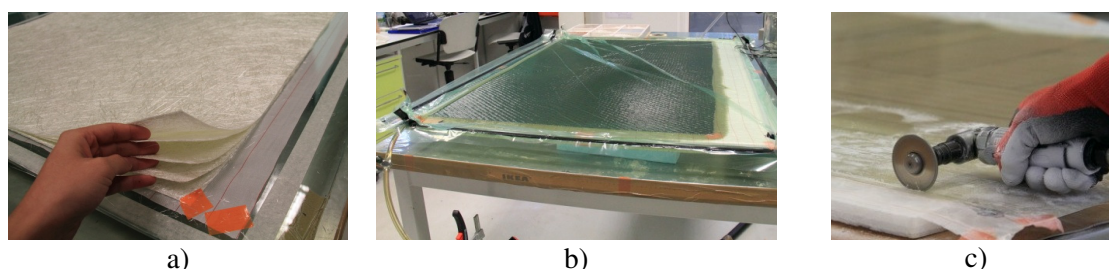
Processo de fabrico dos conectores em GFRP através da técnica de VARTM: a) disposição das camadas de reforço em fibra de vidro; b) injeção da resina; c) corte dos provetes.
